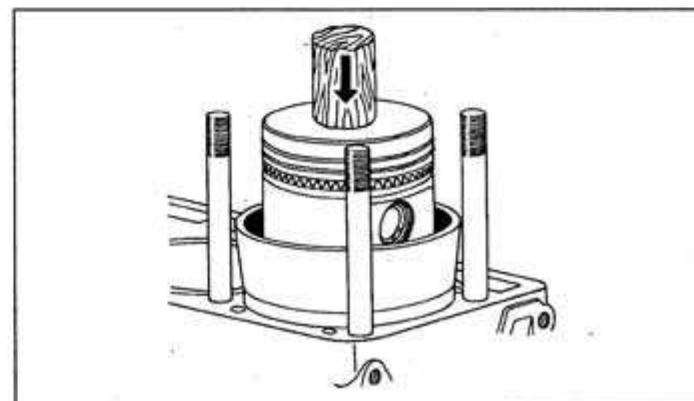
Установка поршня с кольцами в цилиндр с помощью приспособления 5-У-11106
